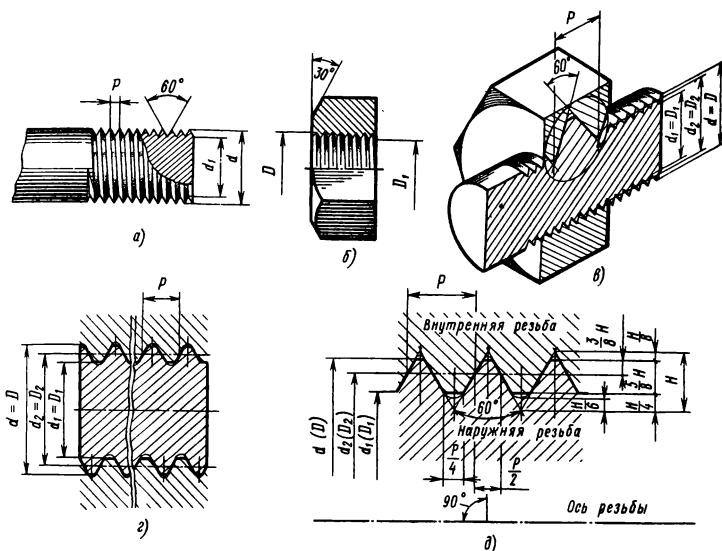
Наружная (а), внутренняя (б) резьба, соединение болта с гайкой (в) и параметры резьбы (г и д)
